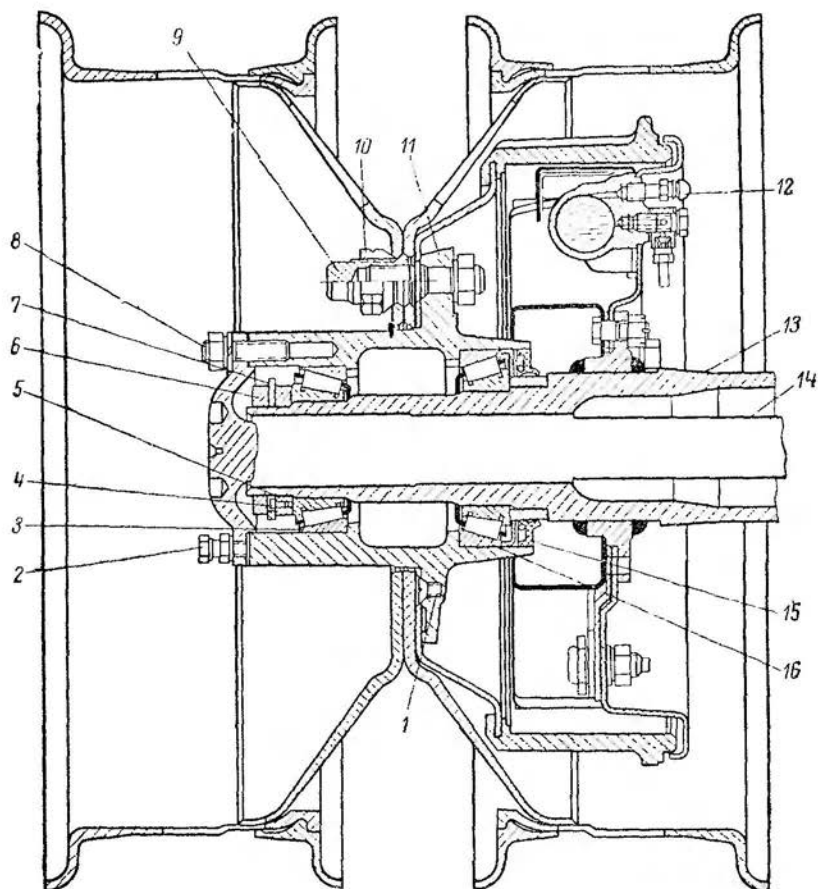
Ступица заднего колеса автомобиля ГАЗ-53А:
